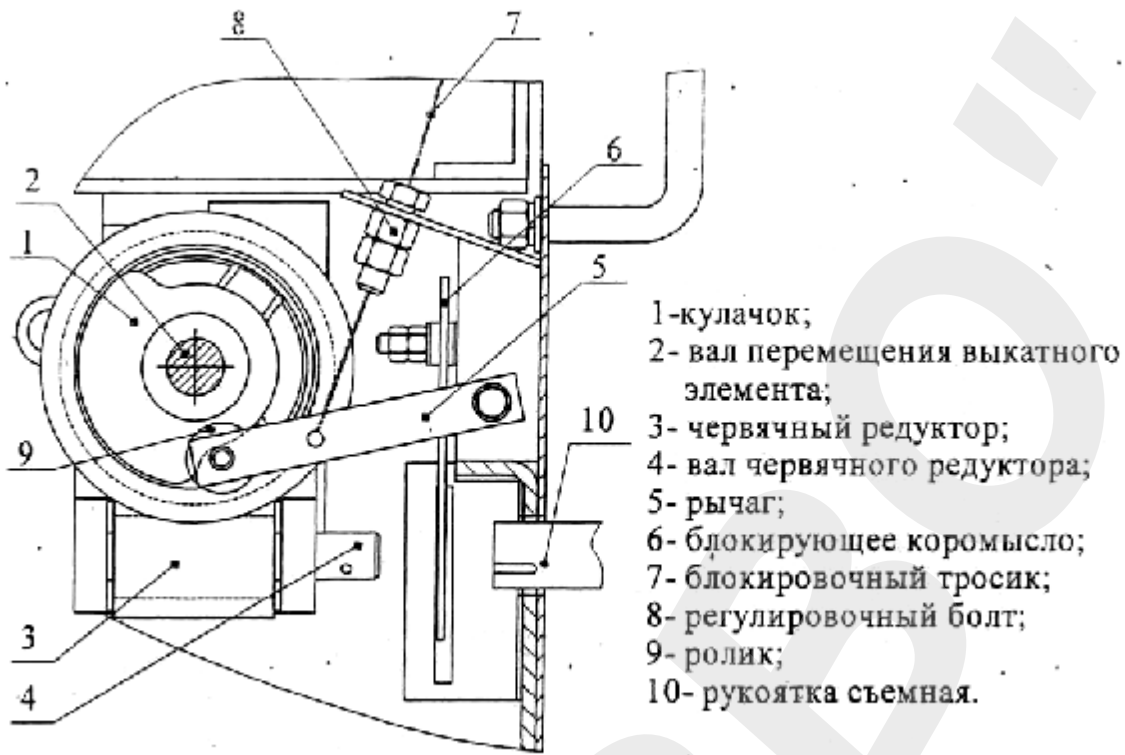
Блокировка выкатного элемента с выключателем ВВМ-10.
